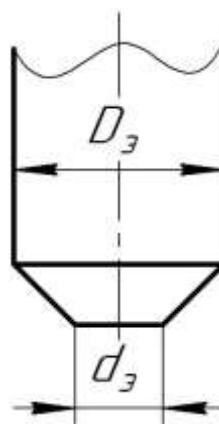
Размеры электрода с плоской рабочей поверхностью.
